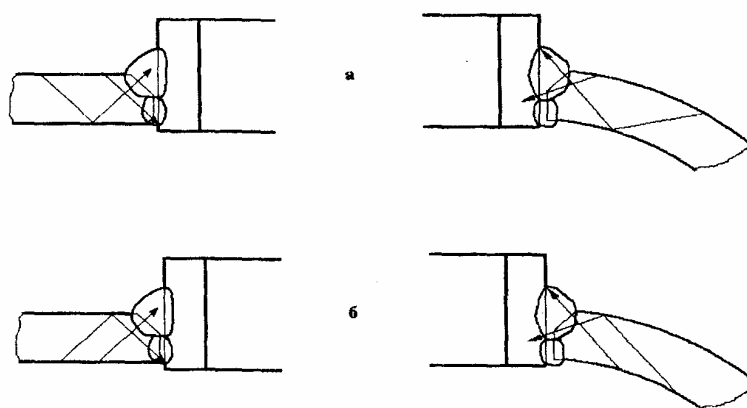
Схема контроля углового сварного соединения штуцера по поверхности корпуса
